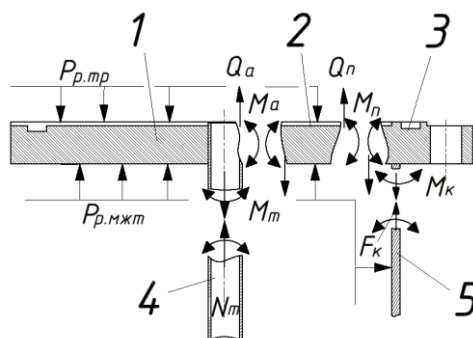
Расчетная схема трубной решетки с нагрузками:
